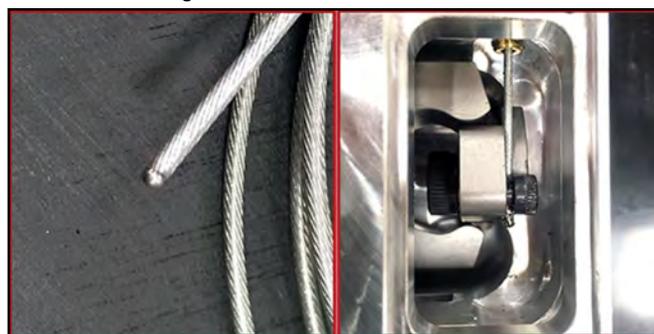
GELÖTETES KABELLENDE (LINKS); KABELLENDE UNTER DER M4-SCHRAUBE BEFESTIGT (RECHTS)
